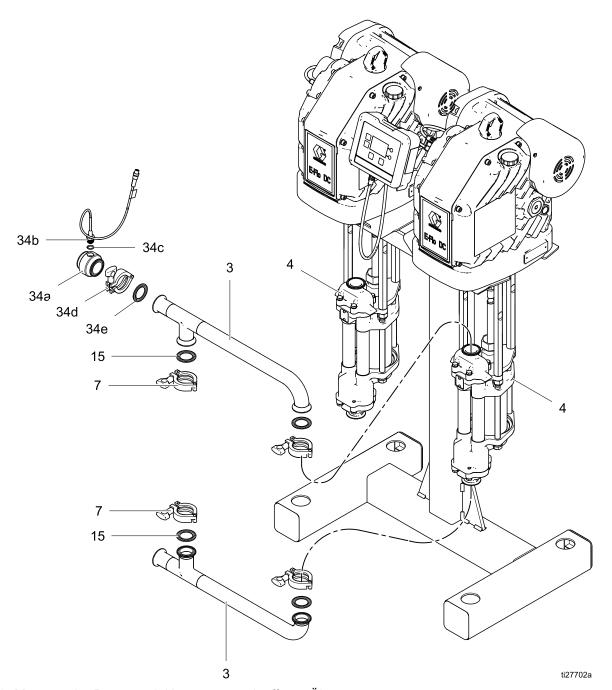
Montage der Pumpe, mit Unterpumpe mit offener Ölertasse
